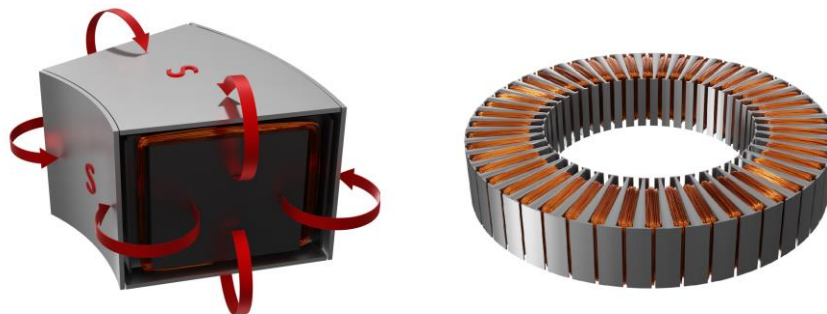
Магнітний «тунель» статора та обмотка статора
